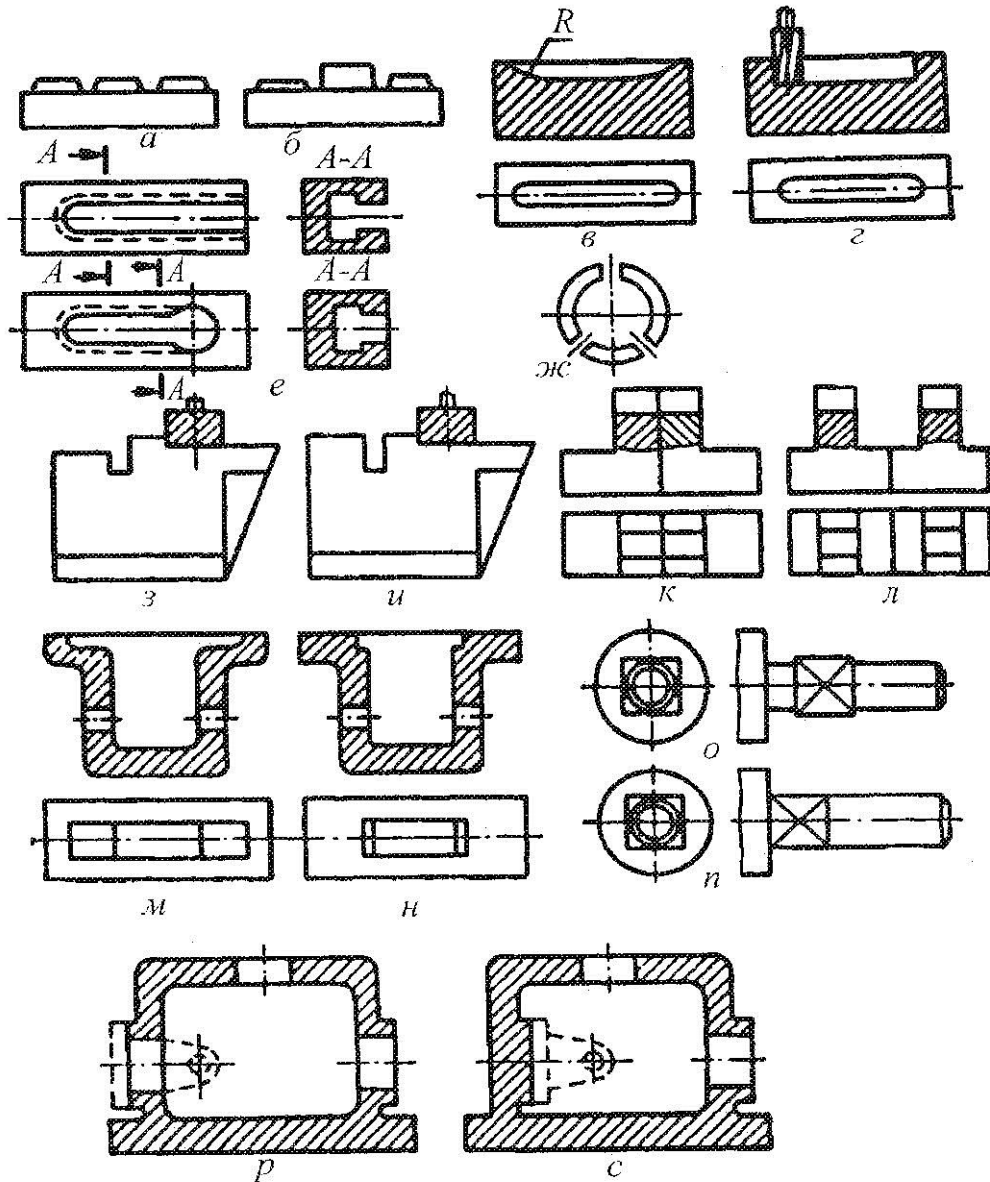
Приклади конструкцій деталей машин, оброблених на фрезерних верстатах
